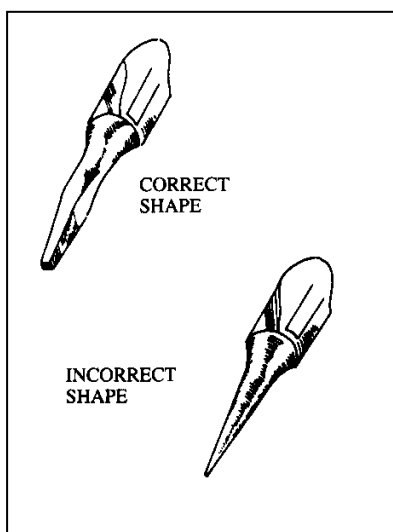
Formas de la punta del cautín. soldadura.
